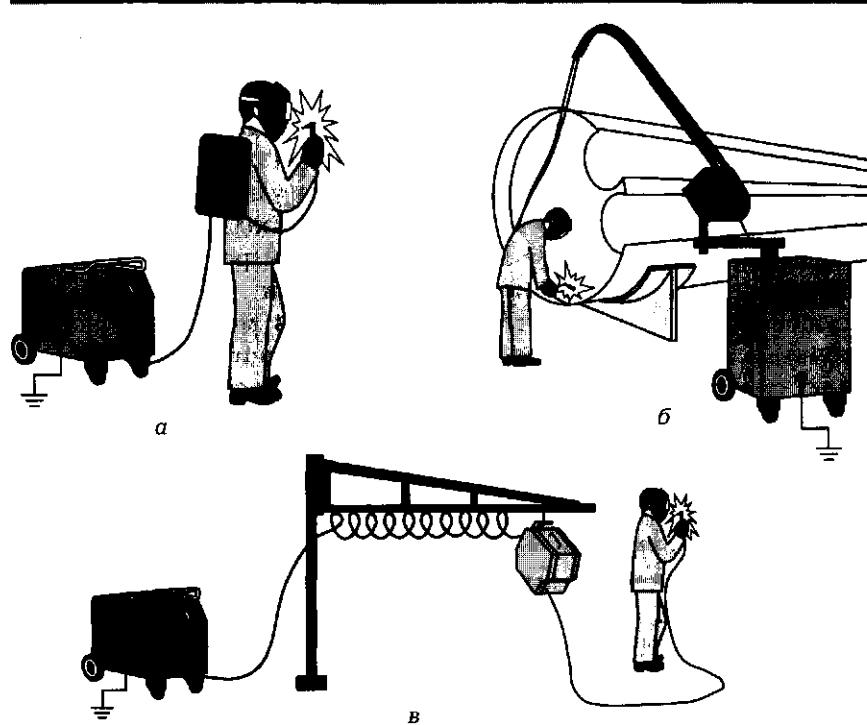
Приемы выполнения сварки полуавтоматом:
